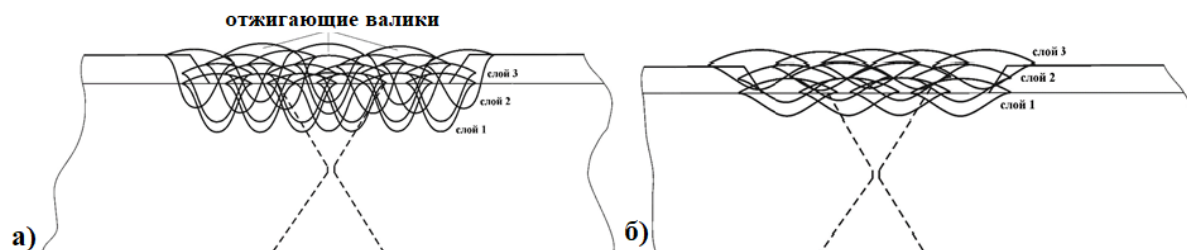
Схема раскладки валиков сварки переходного (слой 1) и плакирующего (слой 2 и слой 3) слоев при автоматической сварке в защитной среде аргона (ИП) [4]:
